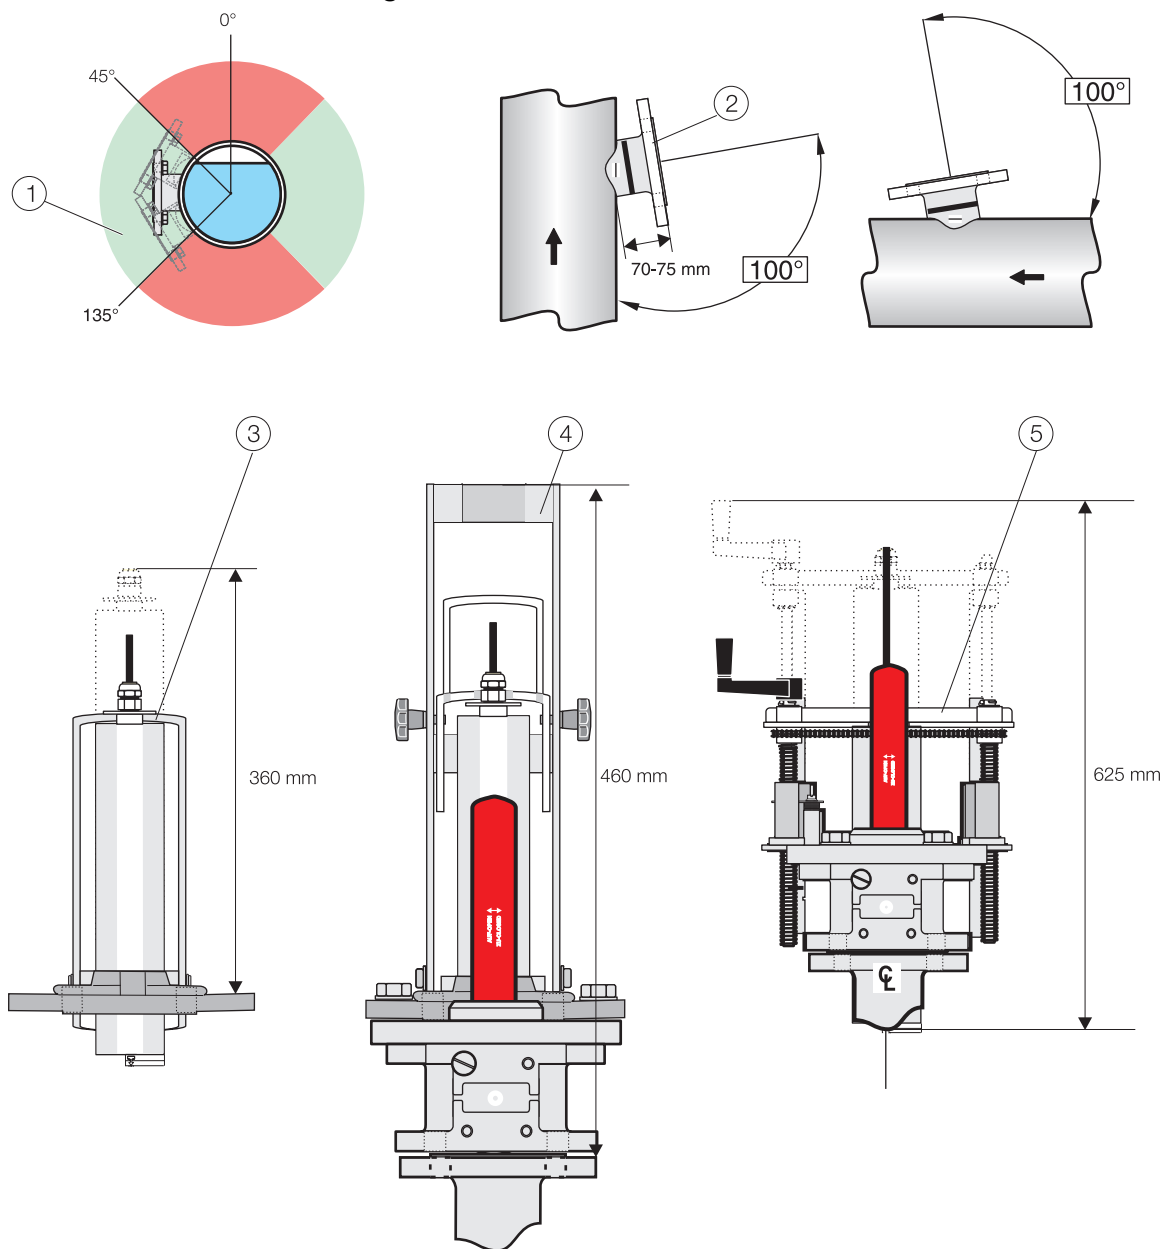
Installationsübersicht Halterung Sensor LZX414...
